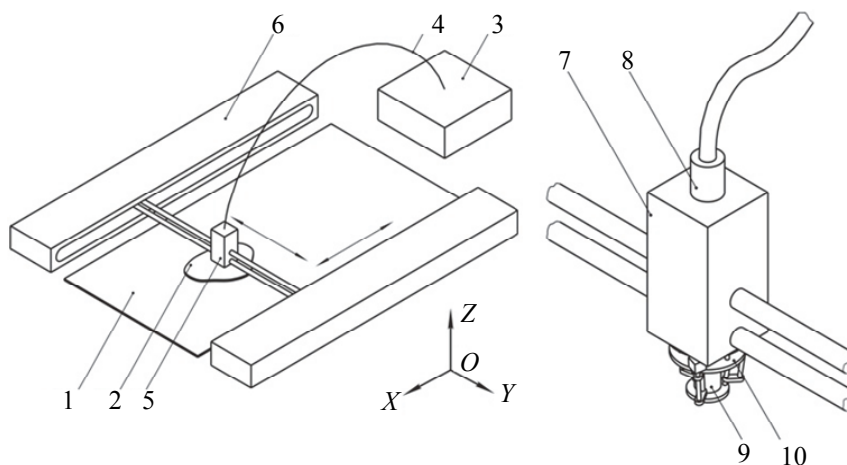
Схема устройства для обработки лазерным излучением: 1 – рабочий стол; 2 – обрабатываемый объект; 3 – источник лазерного излучения; 4 – оптическое волокно; 5 – лазерная головка; 6 – механизм перемещения; 7 – контроллер управления лазерной головкой; 8 – оптический ввод; 9 – коллимирующая система; 10 – модифицированная платформа Стюарта
